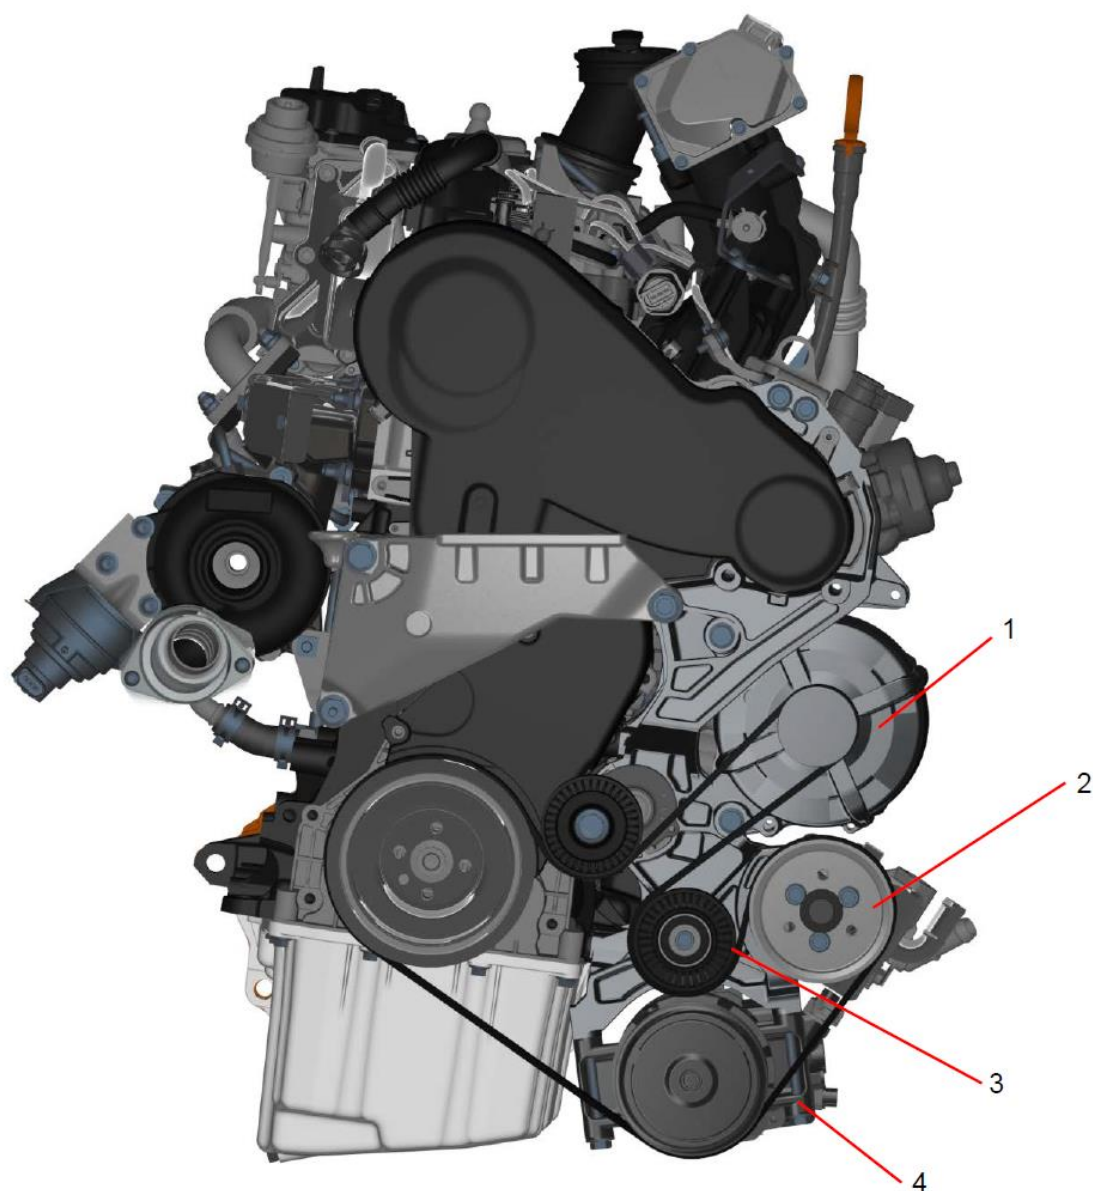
Поликлиновой ременный привод (изображение для двигателя TDI)
